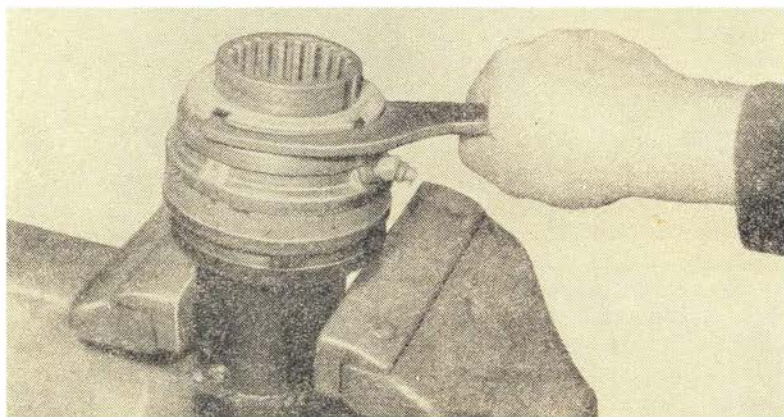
Отвертывание гайки крепления подшипника промежуточной опоры
